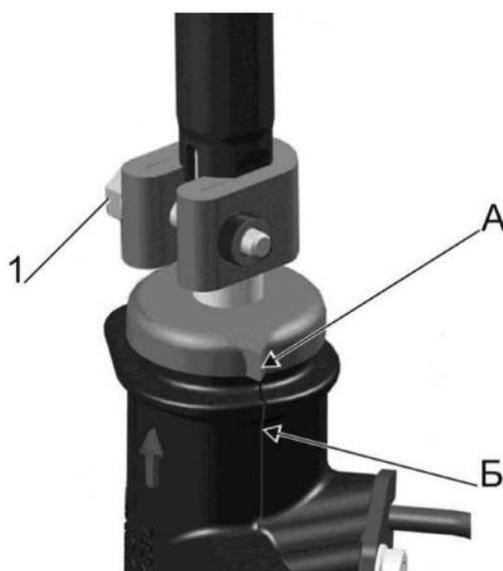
Положение меток на крышке входного вала и корпусе распределителя при среднем положении рулевого механизма: 1 – болт крепления вилки карданного вала
